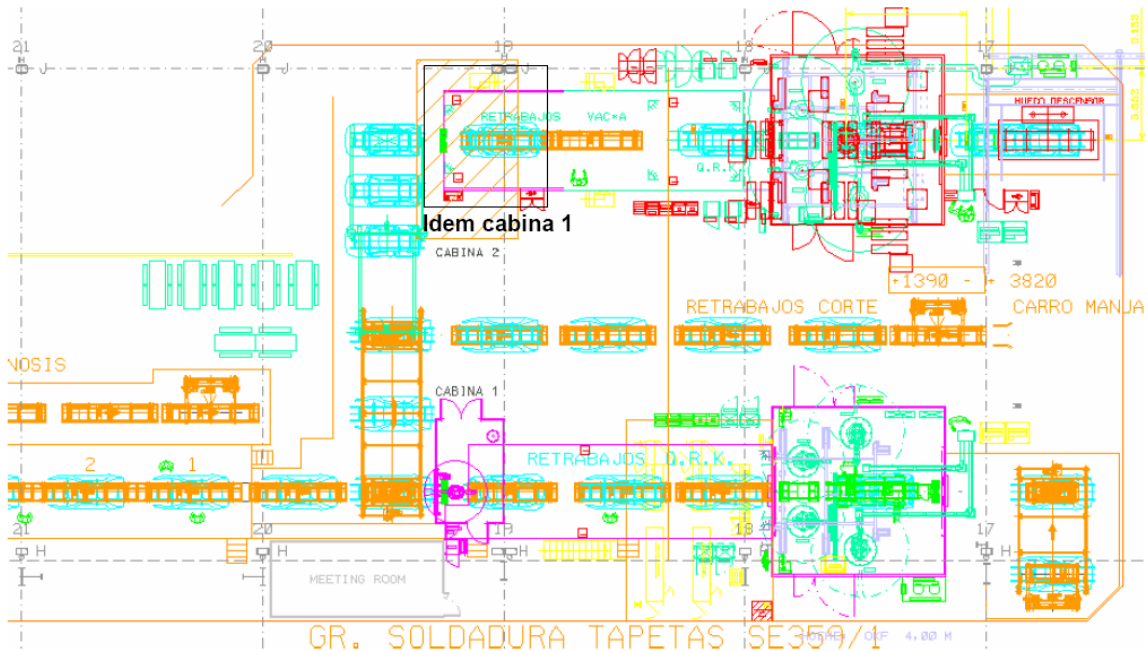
Propuesta B. Dos instalaciones de soldadura
